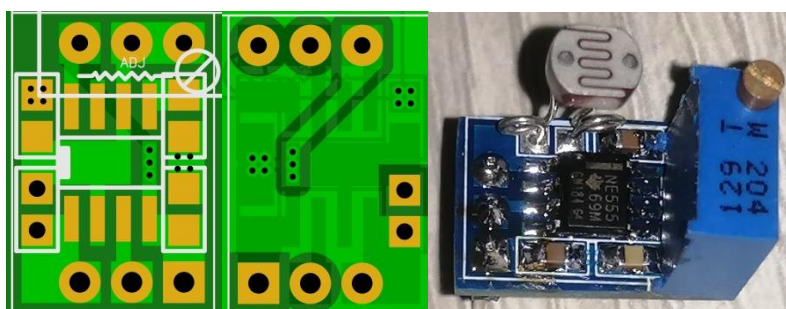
施密特触发光照强度传感器电路 PCB 设计图及实物
